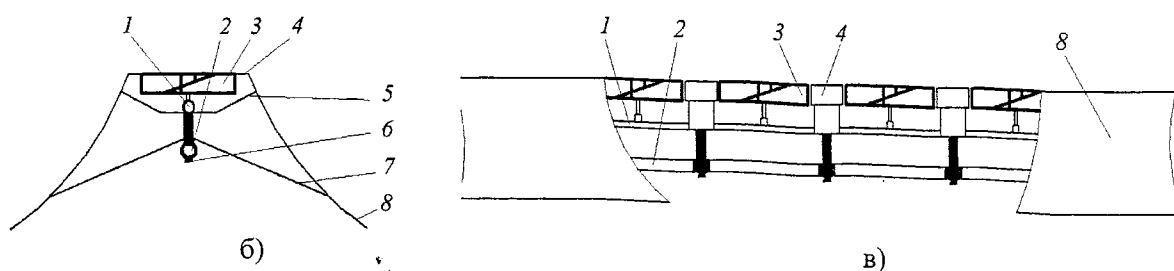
Ветрозащитное устройство комбинированного действия [8]: 1 – несущая конструкция; 2 – распределительная штанга; 3 – вентиляторы; 4 – козырек; 5, 7 – кронштейны; 6 – распылитель; 8 – ветрозащитные щитки
